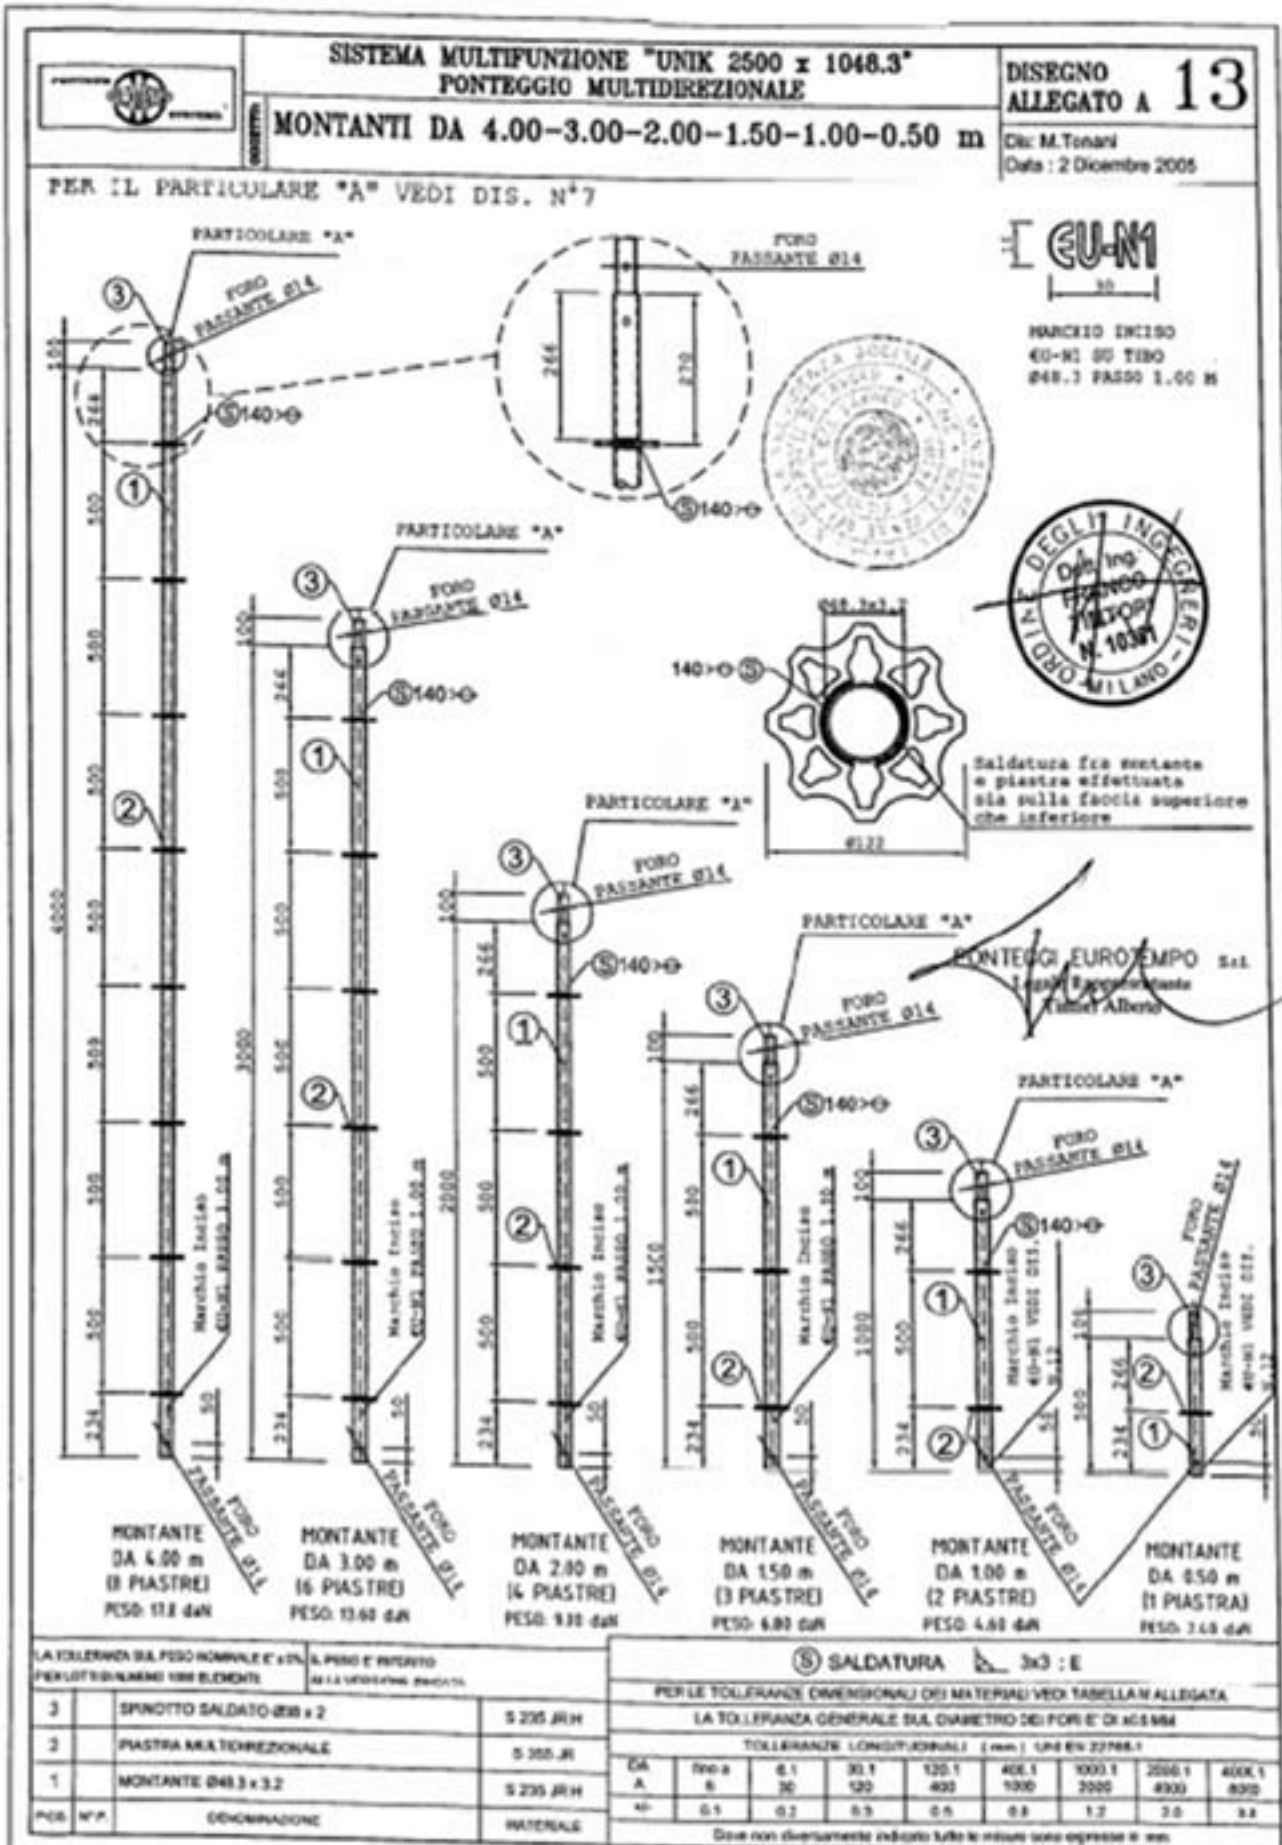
Tubi di dimensione da 50 cm. a 4 m.
